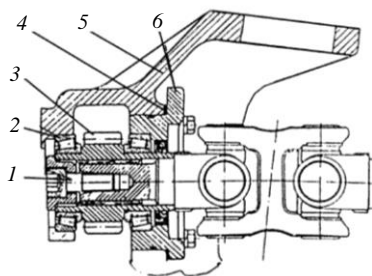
Регулировка подшипников ведущей шестерни колесного редуктора: 1 – болт; 2 – подшипник; 3 – ведущая шестерня; 4 – регулировочные прокладки; 5 – корпус; 6 – стакан
